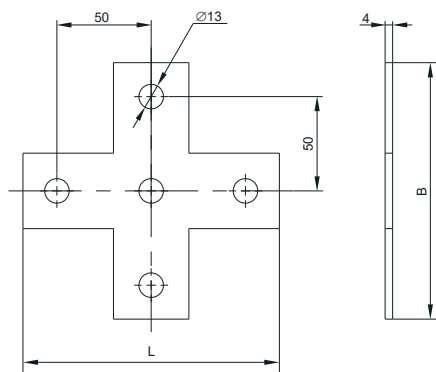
Пластина соединительная Х-образная для STRUT-профиля / Figure I.4 – X-shaped joining plate for STRUT profile
